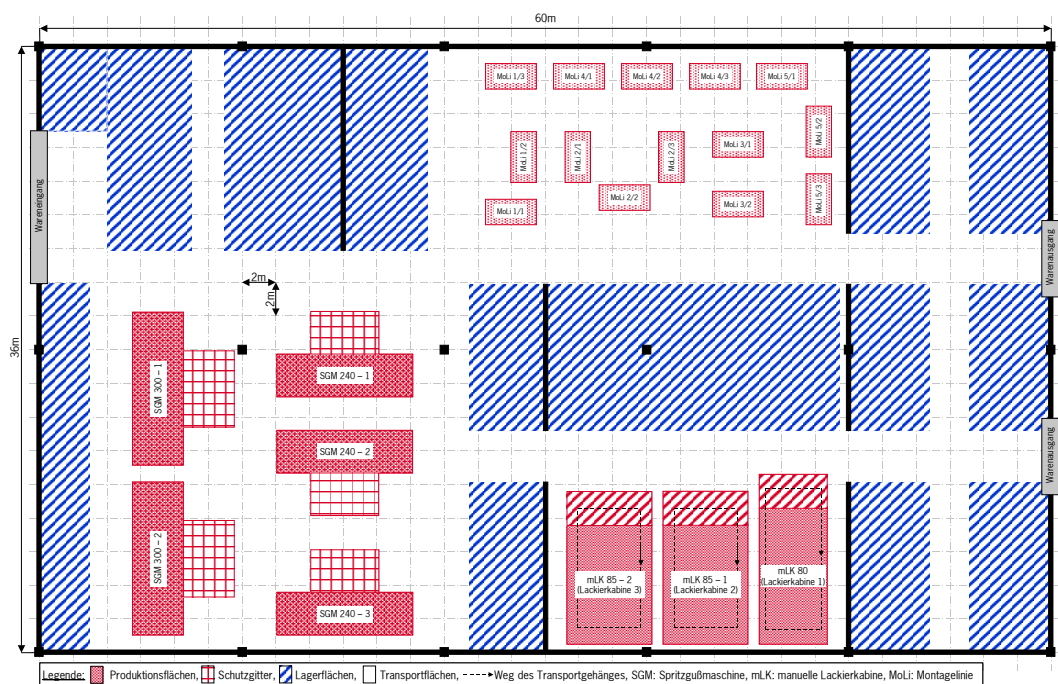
Aufbau des Planspiels LEANLAYOUT
